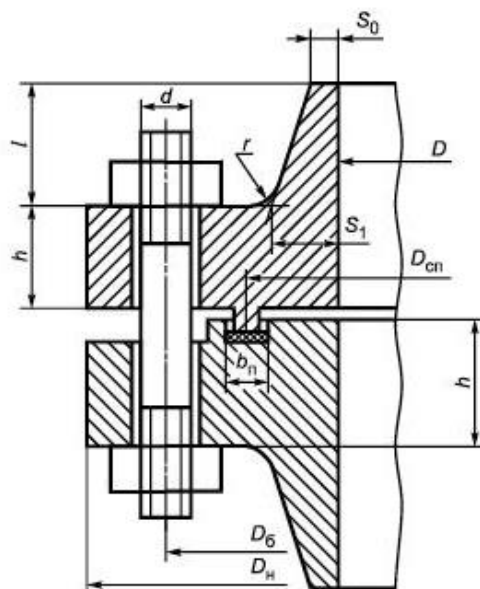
Расчётная схема фланцевого соединения крышки с корпусом с уплотнительной поверхностью типа шип-паз
